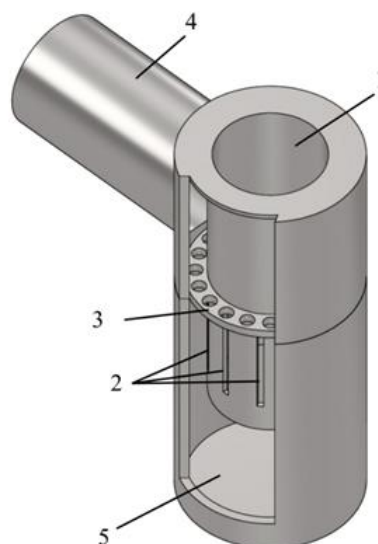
Центробежный классификатор: 1 – патрубок входной; 2 – прорези; 3 – решетка с отверстиями; 4 – патрубок выходной; 5 – бункер
